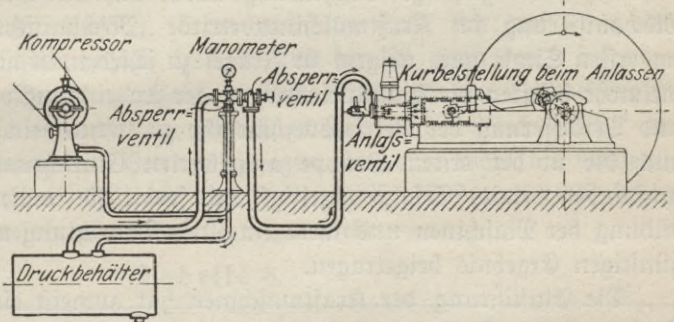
Druckluftanlassvorrichtung für Gasmotoren.
